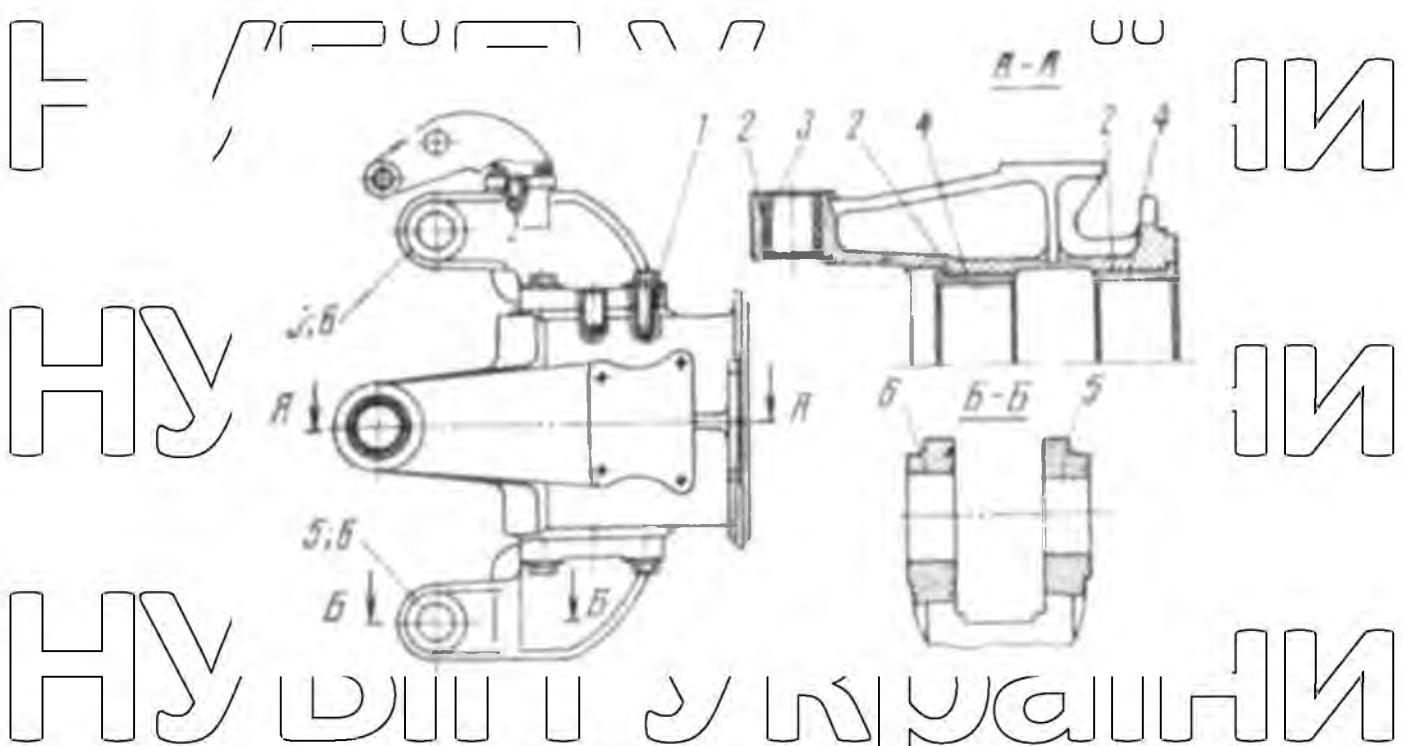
Корпус шарніра 171.30.018-ЗСБ
